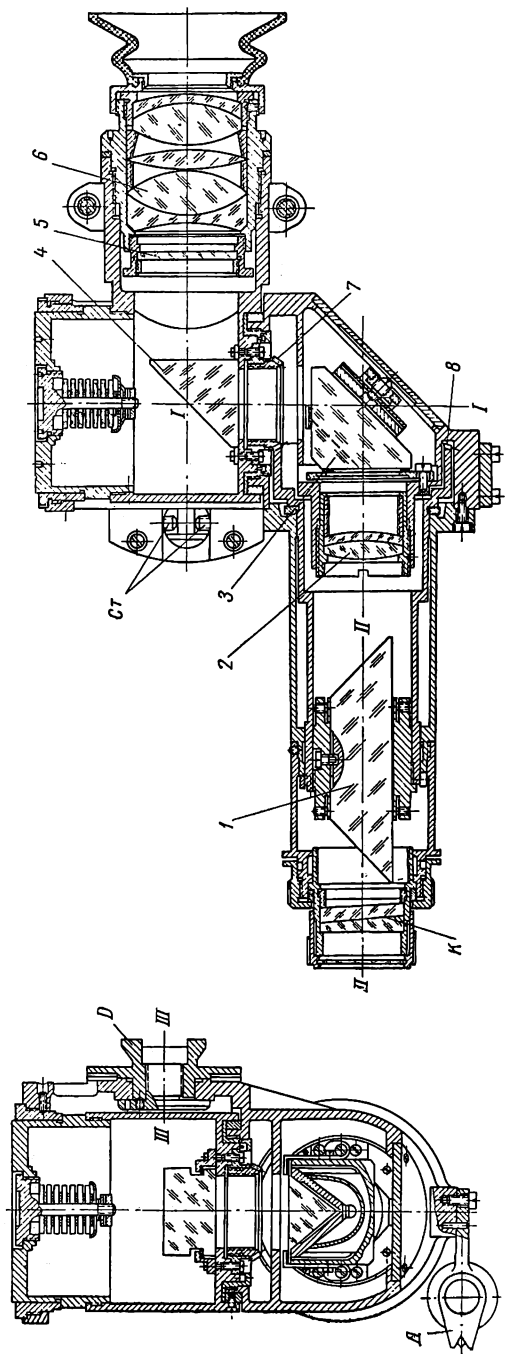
Конструктивная схема коленчатой трубы ПО-1М
